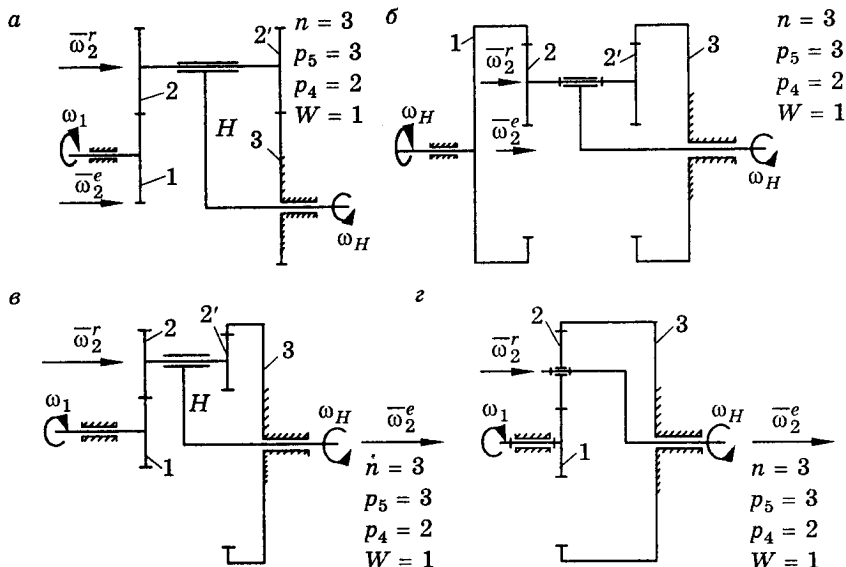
Схемы планетарных редукторов с неподвижной шестерней
